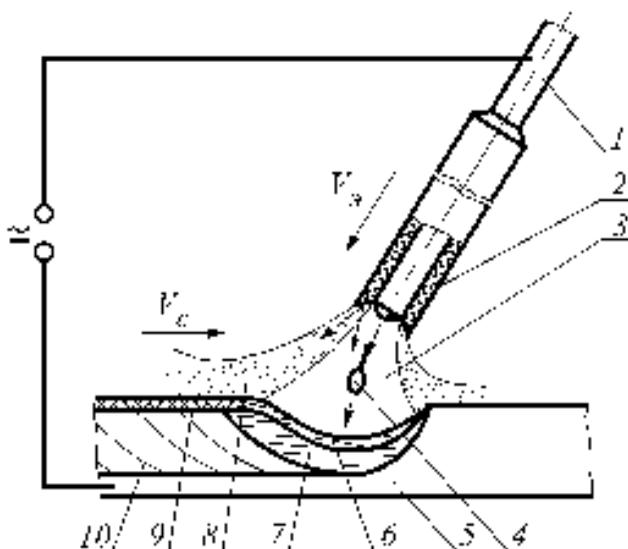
Схема ручной дуговой сварки.
